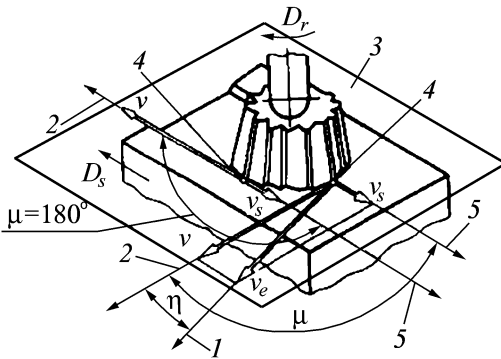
Элементы движений в процессе резания при фрезеровании концевой угловой фрезой:
